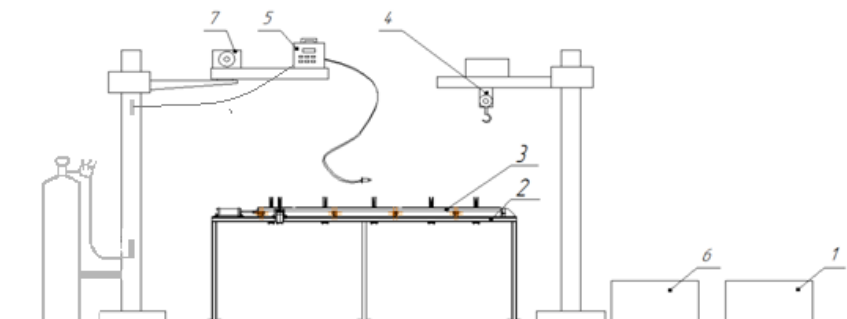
Схема компоновки рабочего места сборки узла №1: 1 – контейнер с собранными подузлами; 2 – сборочно-сварочный стол для сборки узла №1; 3 – собираемый подузел; 4 – консольно-поворотный кран; 5 – инверторный полуавтомат ФЕБ Магма 350; 6 – контейнер для заготовок; 7 – блок подачи проволоки
